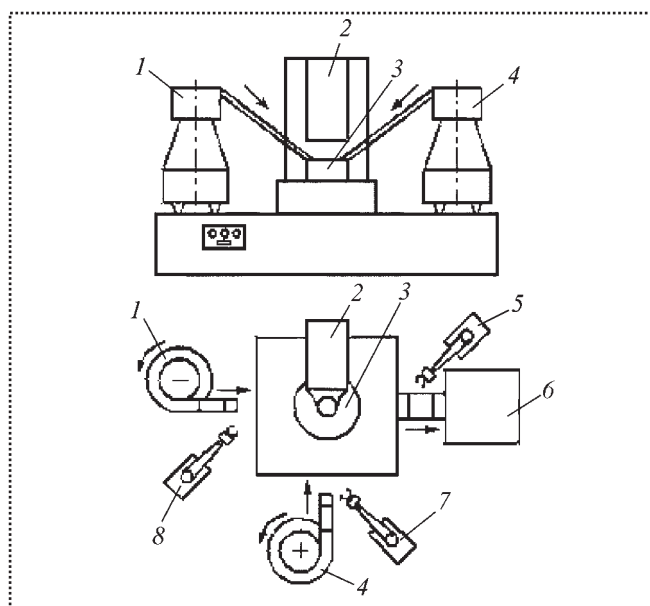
Компоновка сборочного центра для сборки минимального узла из двух деталей:
